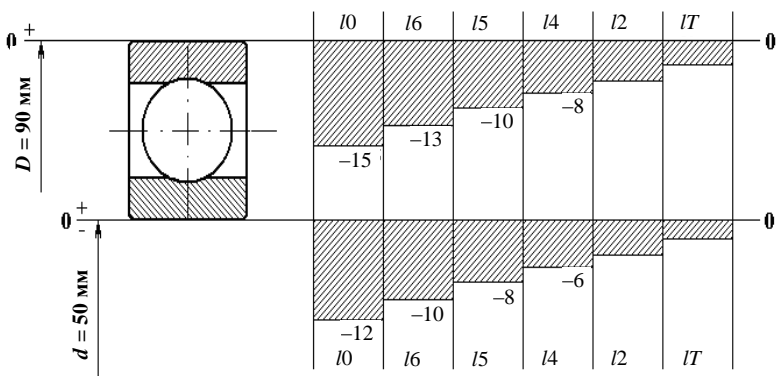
Схема расположения полей допусков по классам точности на средний наружный диаметр наружного кольца и внутренний диаметр внутреннего кольца подшипников качения
